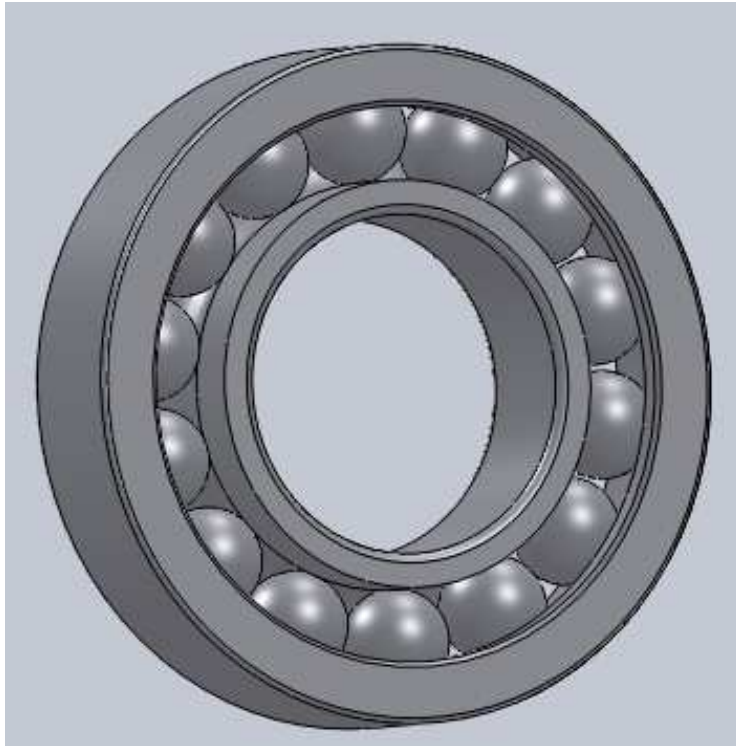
Cuscinetto SKF 7208 BECBJ
